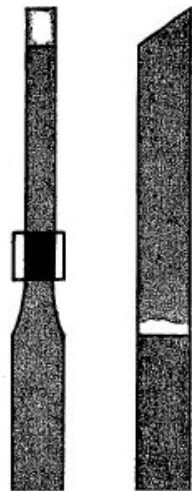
Plattenstahl mit stumpfem Schneidewinkel
